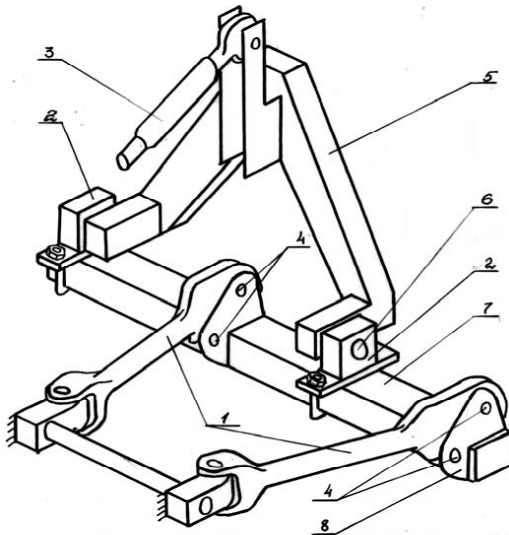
Схема корегуючого пристрою для асиметричного агрегування просапних сівалки і культиватора [45, 50].
